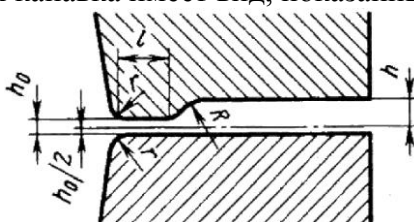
Вид облойной канавки при штамповке на прессах
